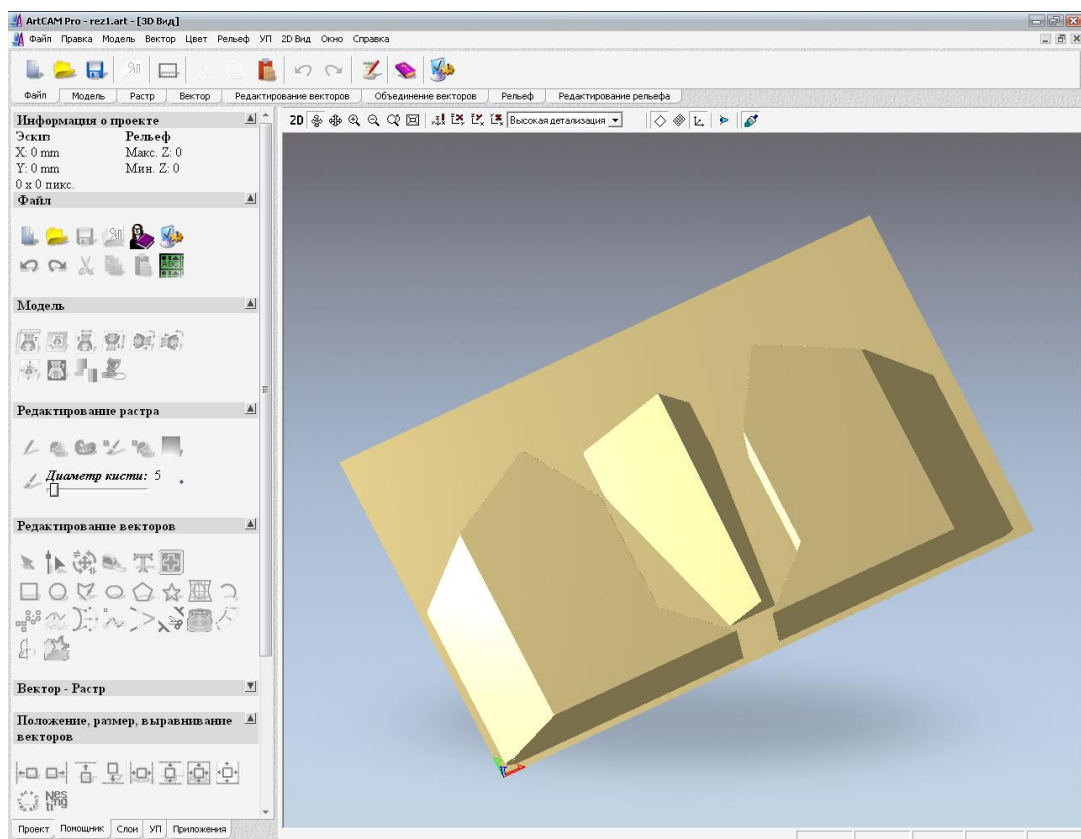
Деталі, що отримуються з першої заготовки, розташовані на робочій площині
